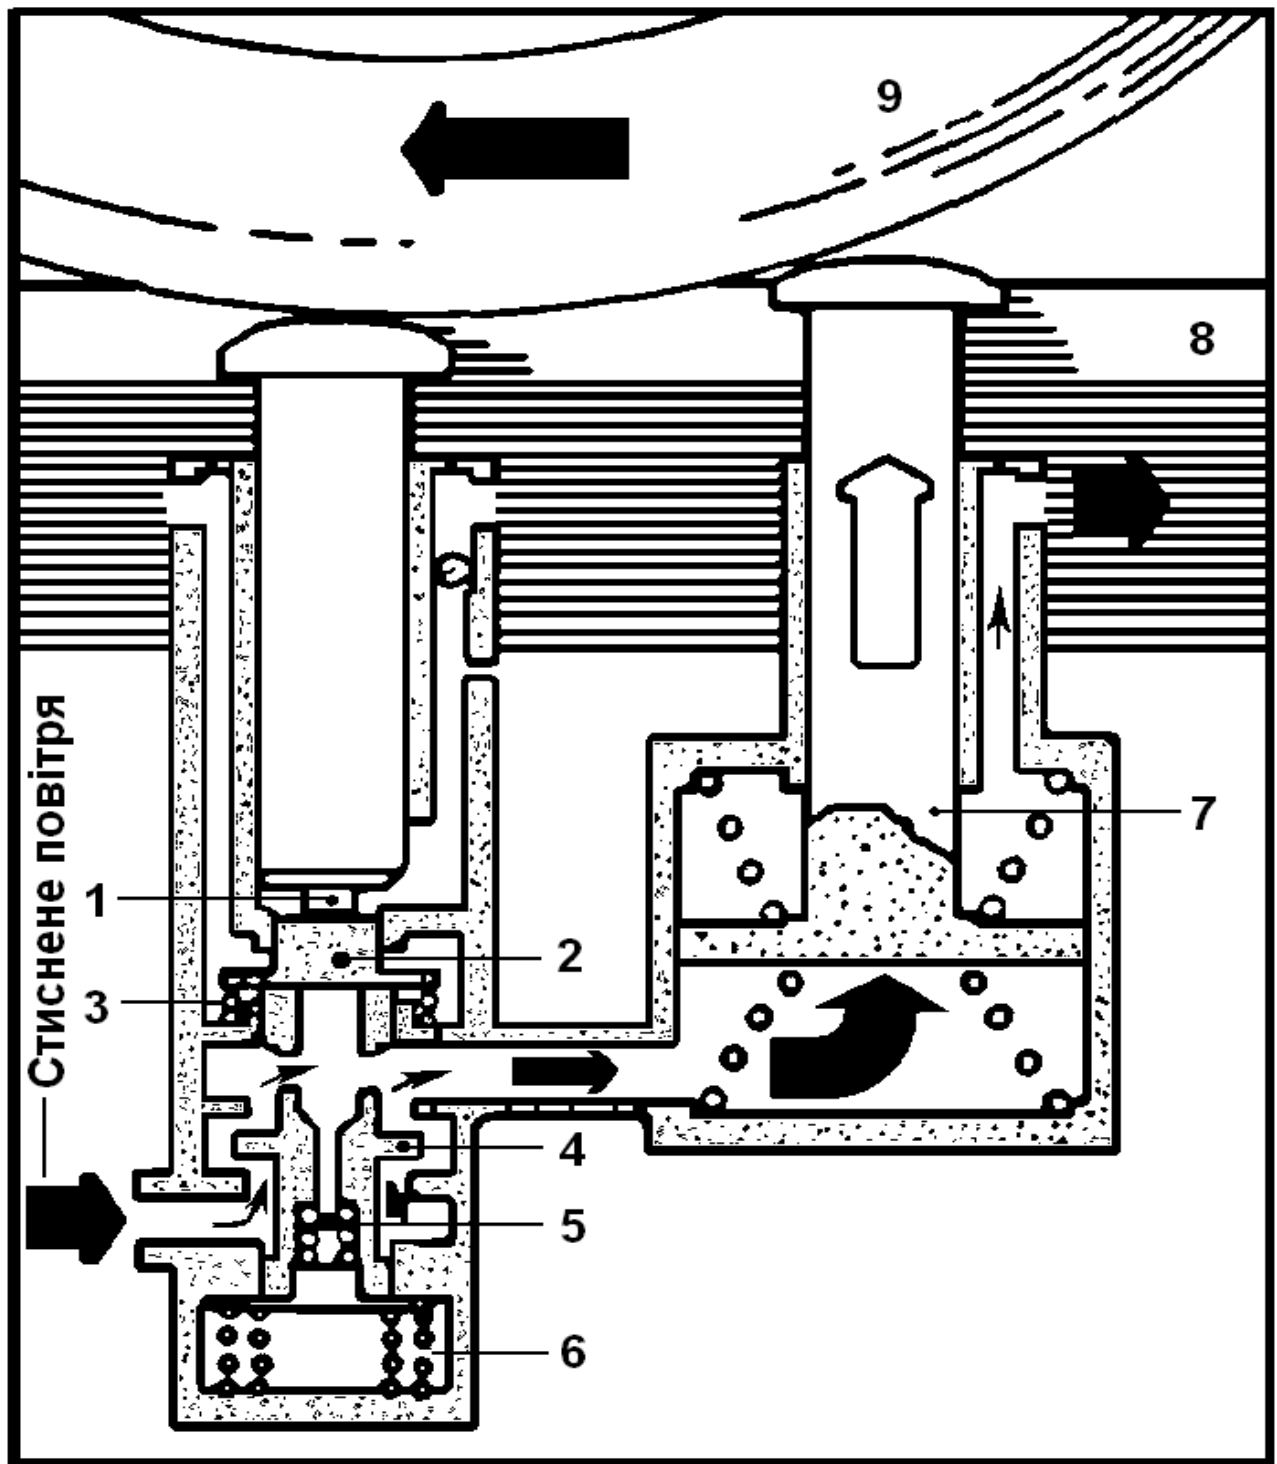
Точковий вагонний прискорювач-уповільнювач:
